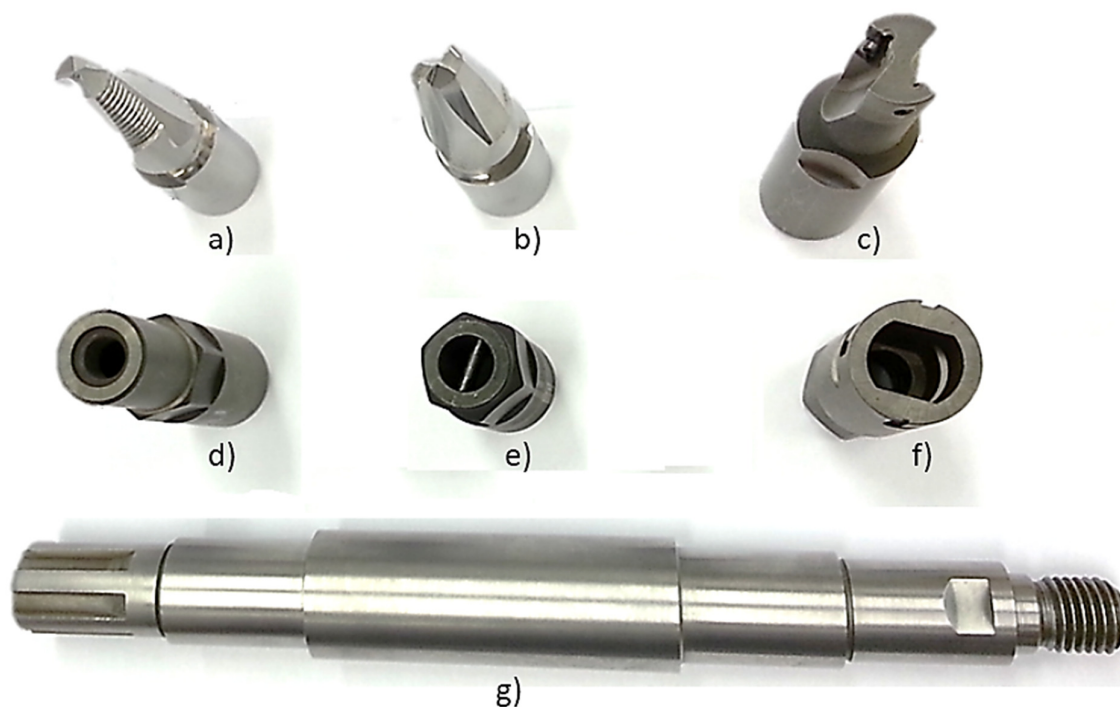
Componentes e acessórios da UPPAX. a) Broca cônica escalonada, b) fresa cônica, c) fresa de topo, d) mandril para processamento de pinos roscados, e) mandril para fixação de pinos consumíveis pelo método FTPW, f) mandril para a fixação de pinos consumíveis pelo método FPPW e g) eixo do cilindro de reparo.
